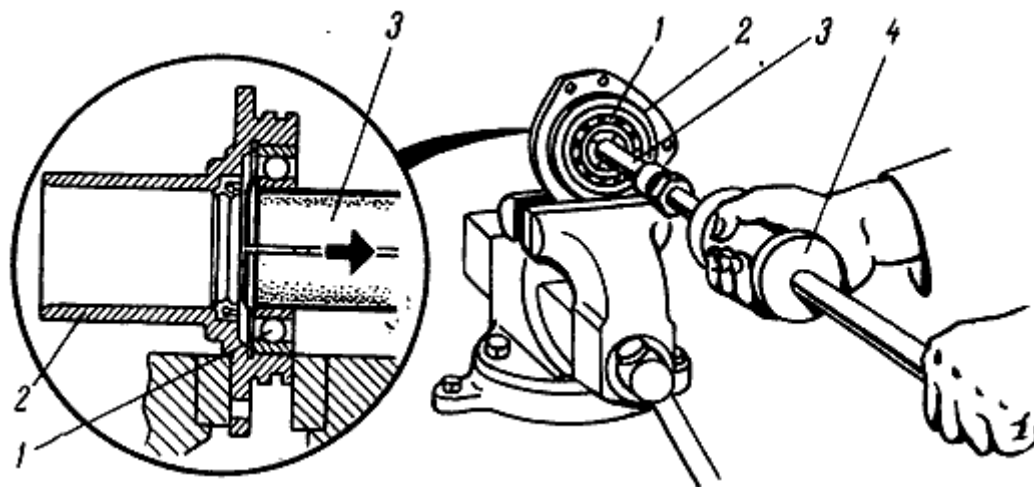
Выпрессовка подшипника из кронштейна отводки тормозка:
